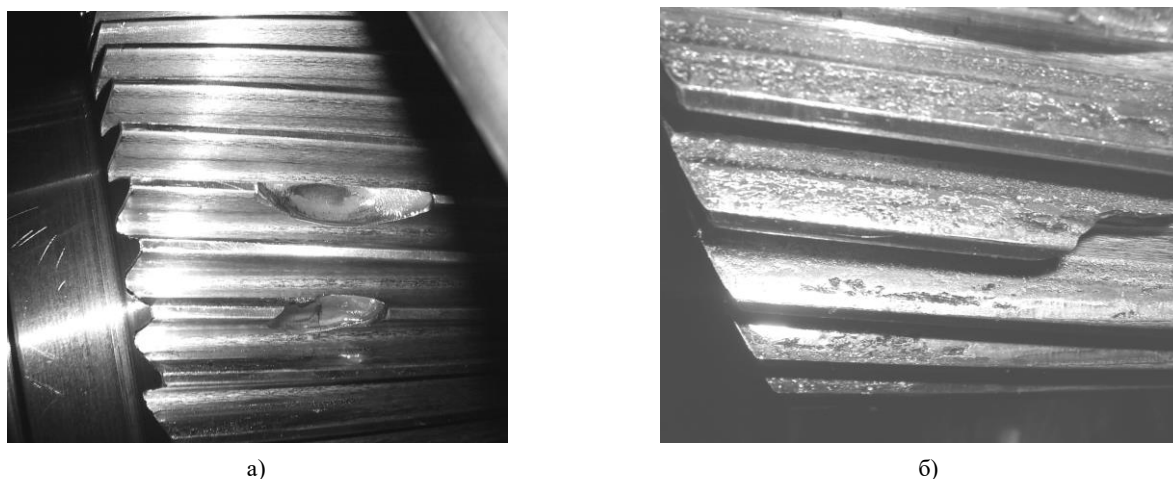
Дефекты поверхности ведомых зубчатых колес:
